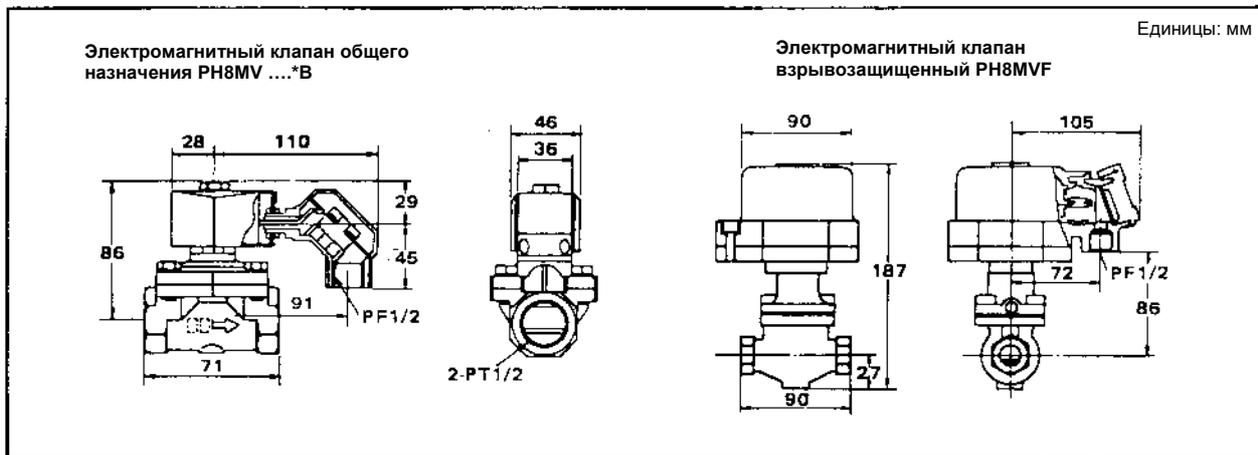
Электромагнитный клапан для очистки с помощью струи / щетки – Внешние размеры
